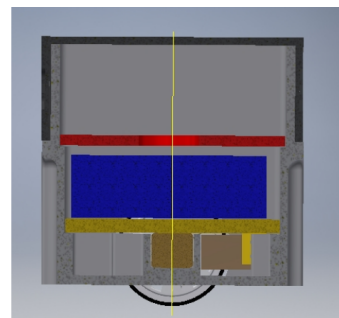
Vista perpendicular com corte transversal do modelo da estrutura.
